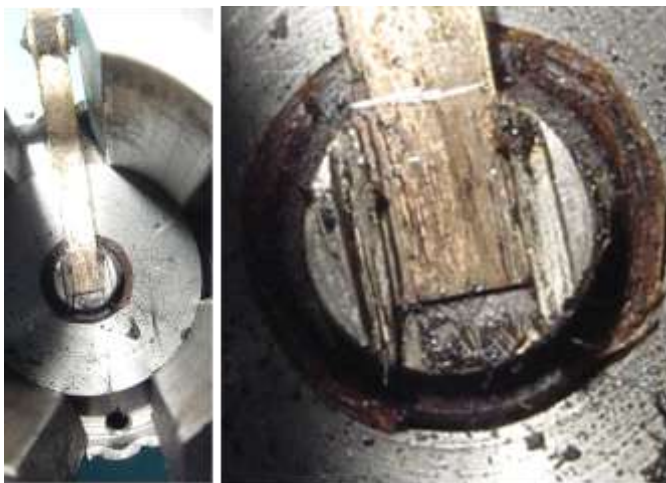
Befestigung der Kontaktfeder am Kontaktbolzen
